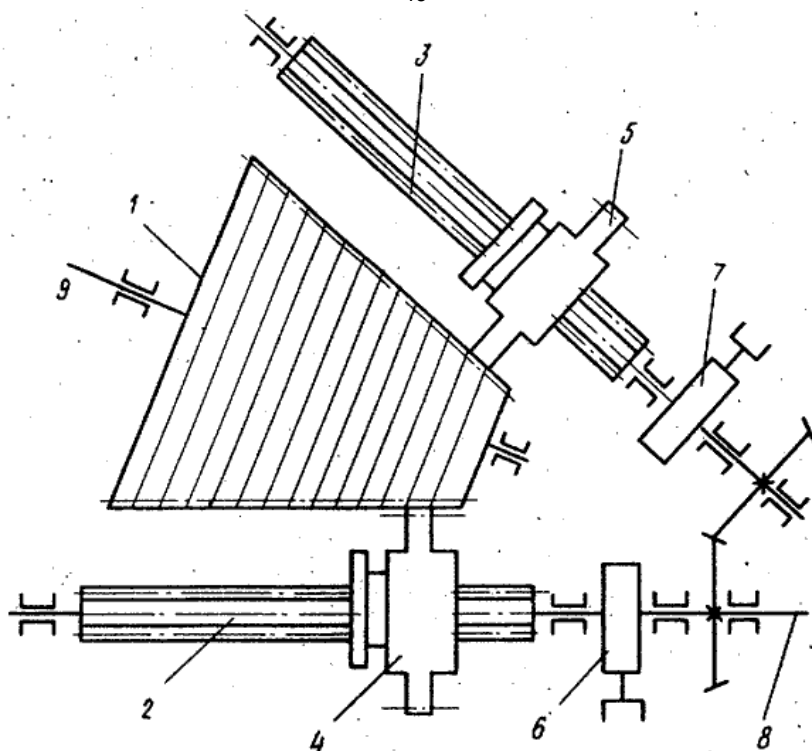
Зубчатий варіатор: 1 – блок евольвентно-конічних коліс; 2 – основний шліцевий вал; 3 – додатковий шліцевий вал; 4, 5 – зубчасті колеса; 6 – муфта; 7 – додаткова електромагнітна муфта; 8 – вал ведучий
